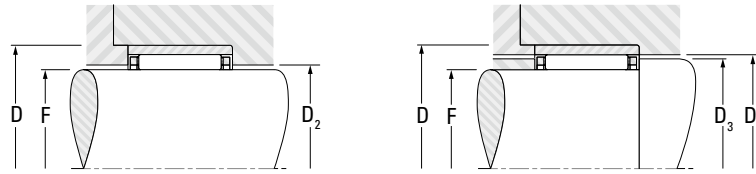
im Gehäuse geführt (links) auf der Welle geführt (rechts)
